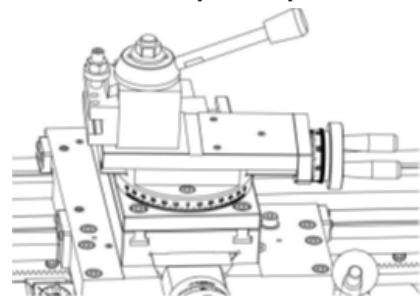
Опциональный резцедержатель быстрой смены инструмента
